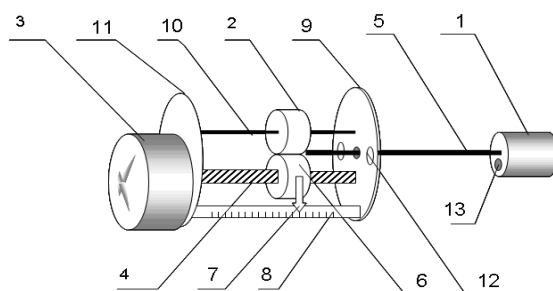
Механизм движения приемника КСИ: 1- ПСИ; 2-опорная втулка; 3- электродвигатель; 4- шаговая штанга; 5-штанга приемника; 6-несущая втулка; 7-указатель шкалы; 8-шкала позиции ПСИ; 9 - крепежный диск; 10-штанга опорной втулки; 11- крепежный элемент двигателя; 12- отверстие для крепления фокусных штанг; 13-отверстие для подключения потребителя.
